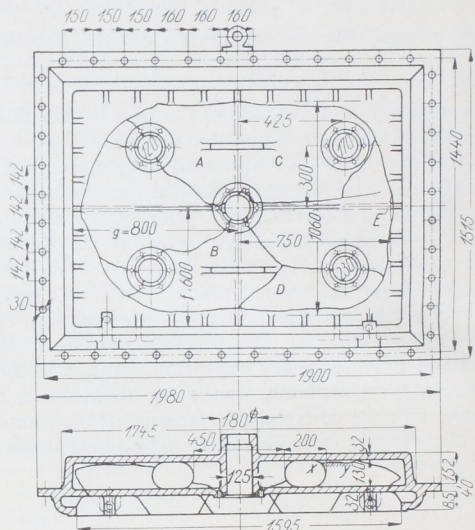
Bruch eines Schieberkastendeckels einer Walzenzugmaschine. Nach Bach. M. 1:30.
